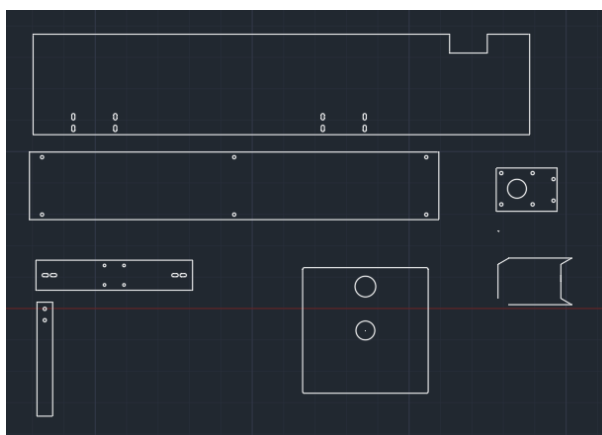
Archivo para realizar el corte de la plancha (Alimentador)
